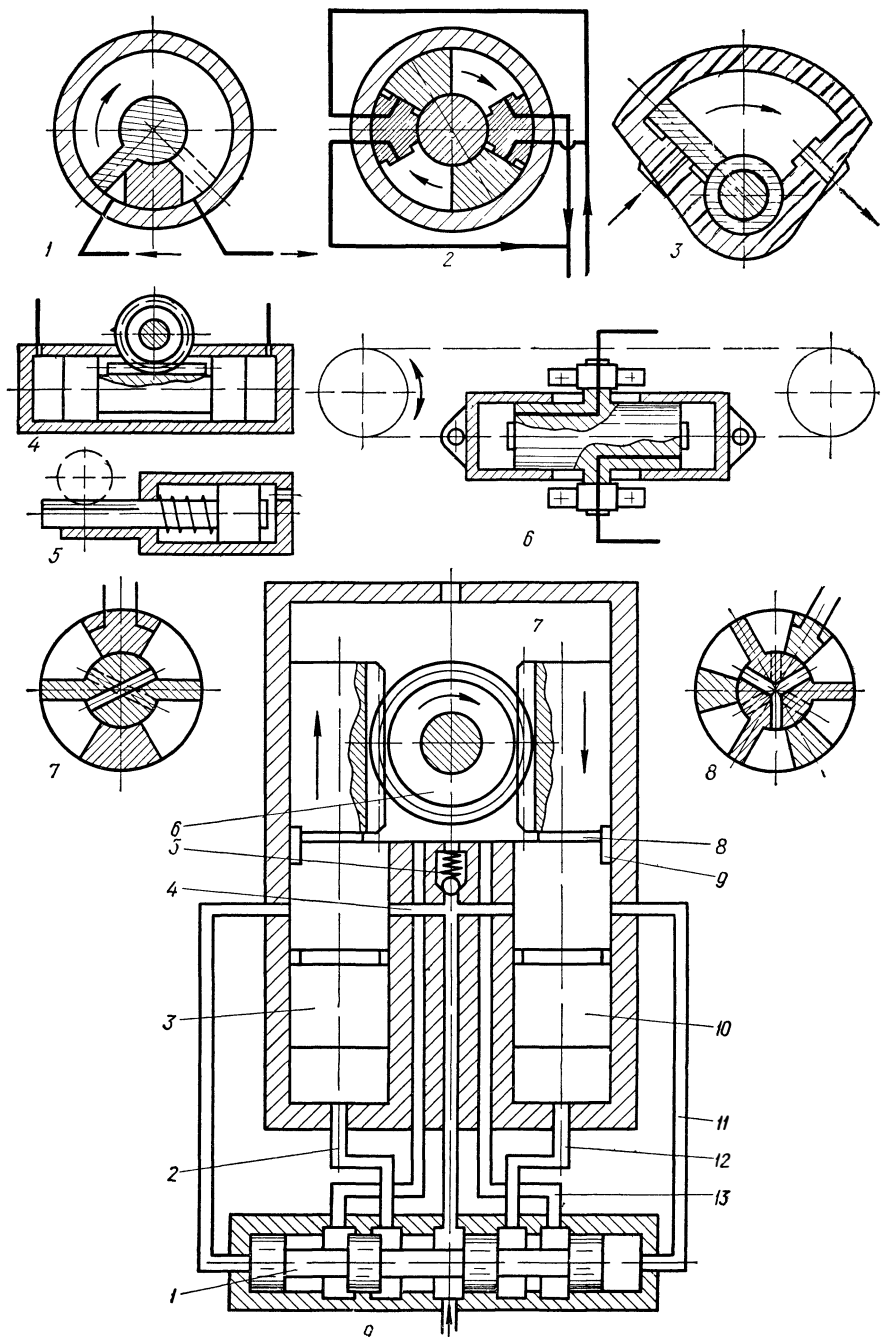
Схемы цилиндров, предназначенные для возвратно-поворотных движений
